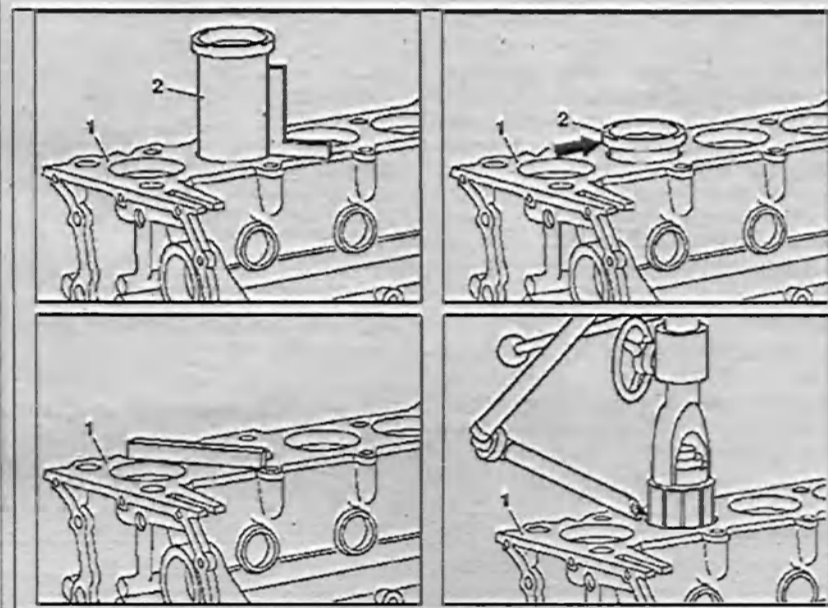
Установка гильзы: 1 - Блок цилиндров, 2 - Гильза.
